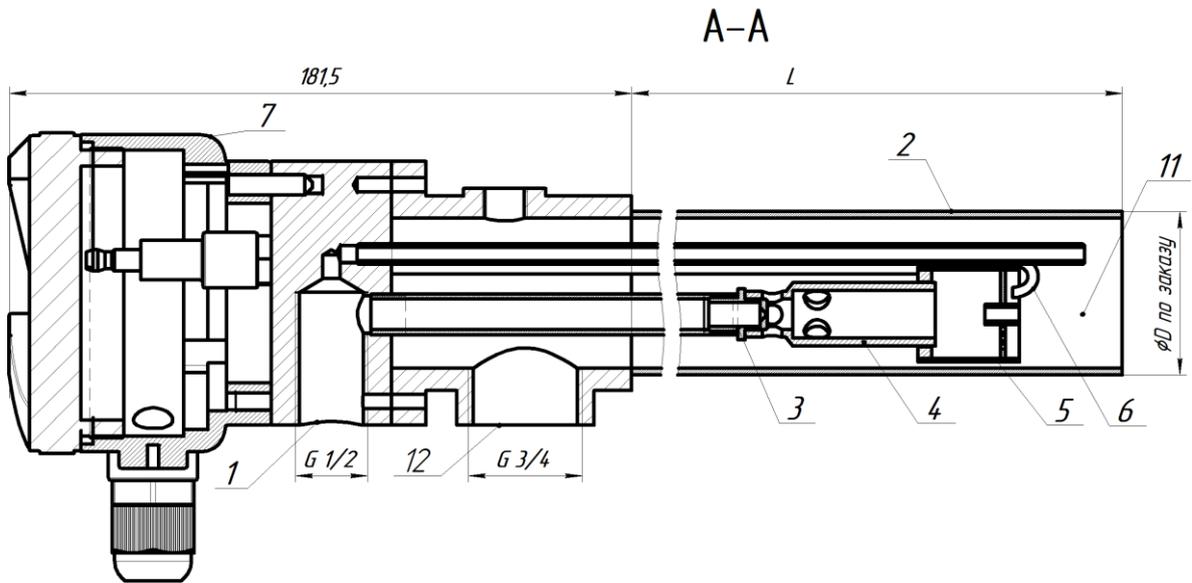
Устройство и габаритные размеры ЗИГ-32(38)-IP65 L
